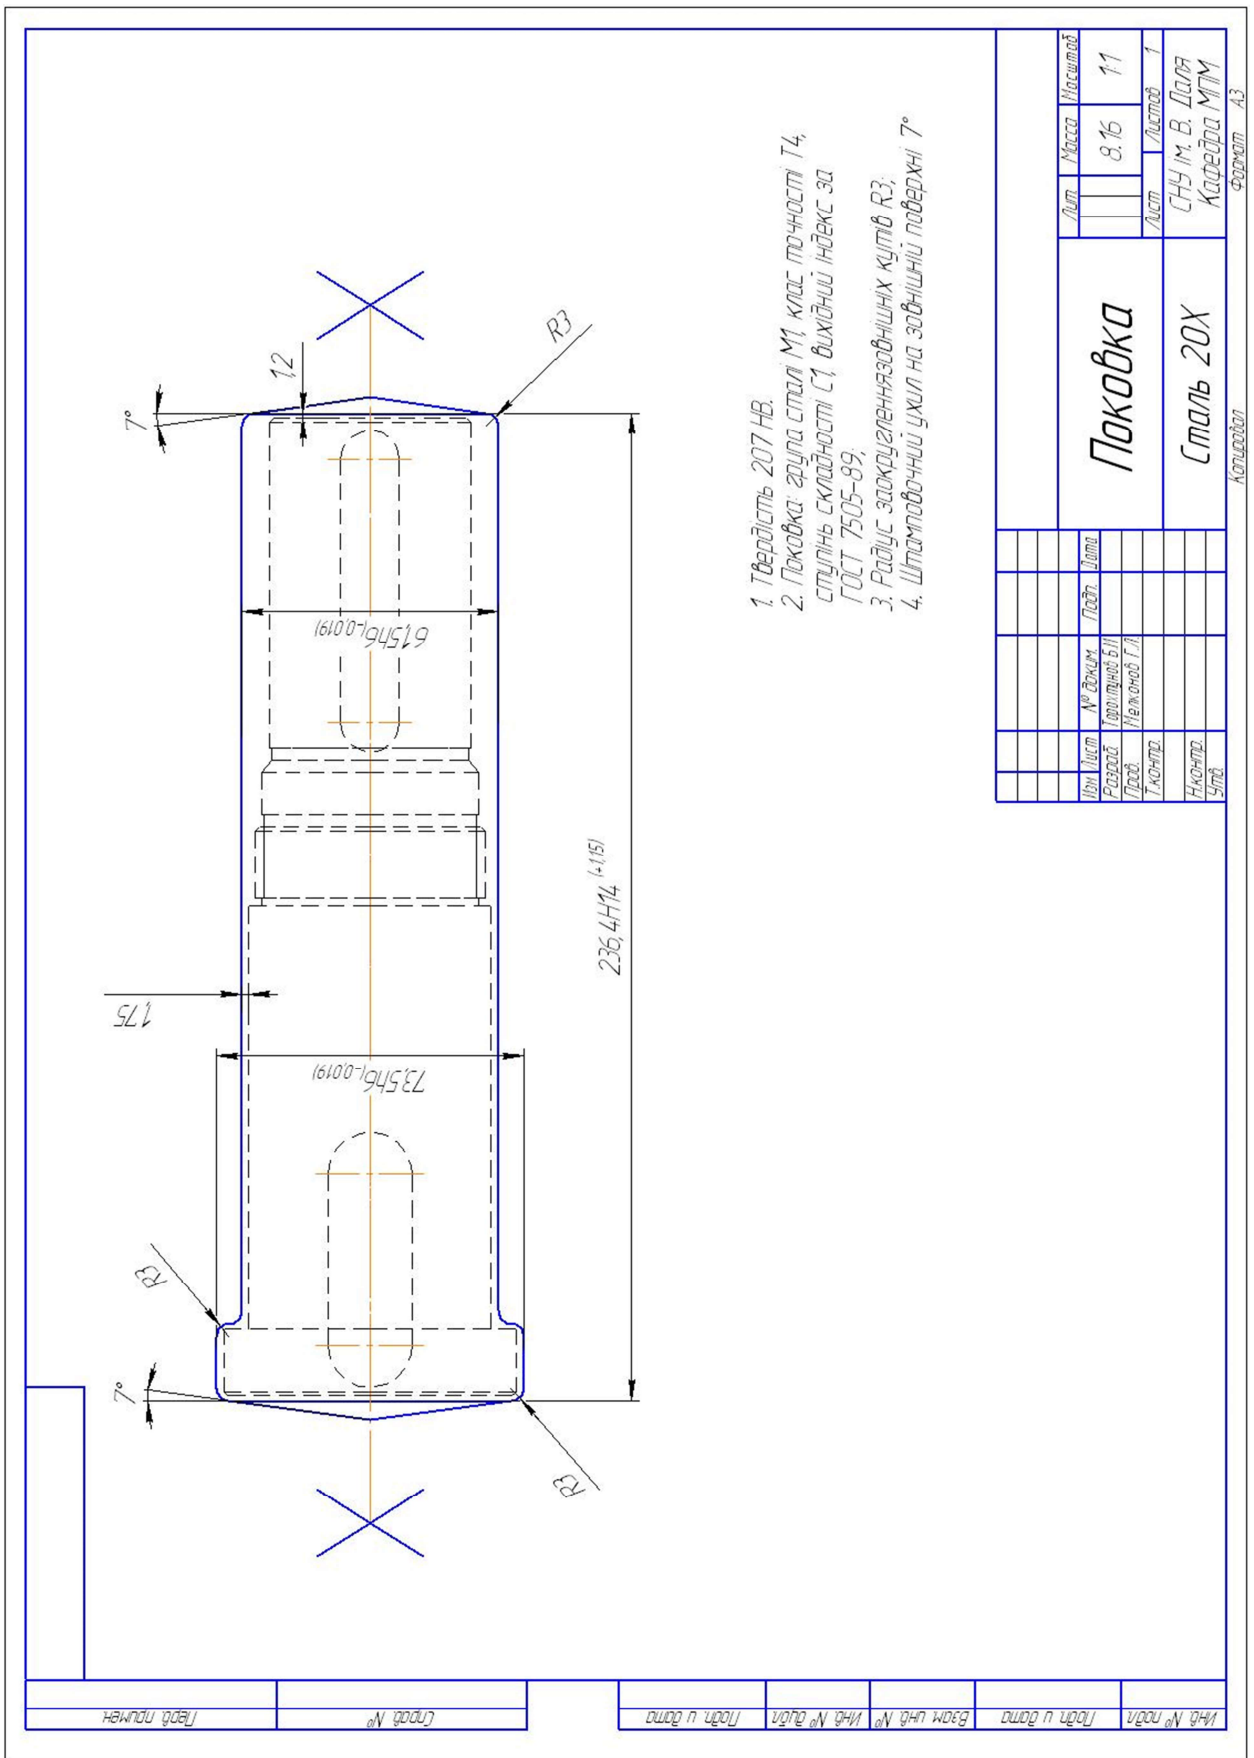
Приклад креслення заготовки деталі «Вал»
